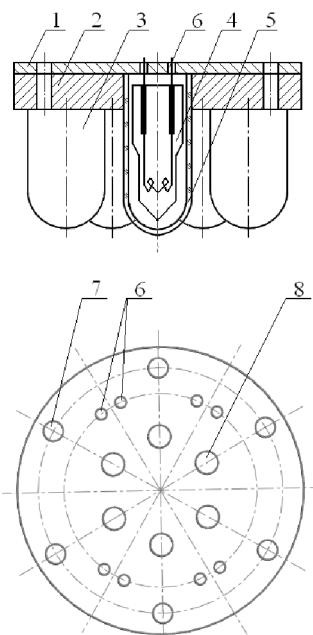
Конструктивная схема оптического наконечника семилампового излучателя для проплавления канала в СЖК: 1 – текстолитовая шайба; 2 – шайба из дюоралюминия с отверстиями для установки галогенных ламп; 3 – кварцевый корпус излучателя; 4 – галогенная лампа; 5 – прозрачная стенка кварцевого корпуса; 6 – отверстия для электрических проводов; 7 – отверстия для крепления шайб; 8 – отверстия для пропускания жидкой фазы
